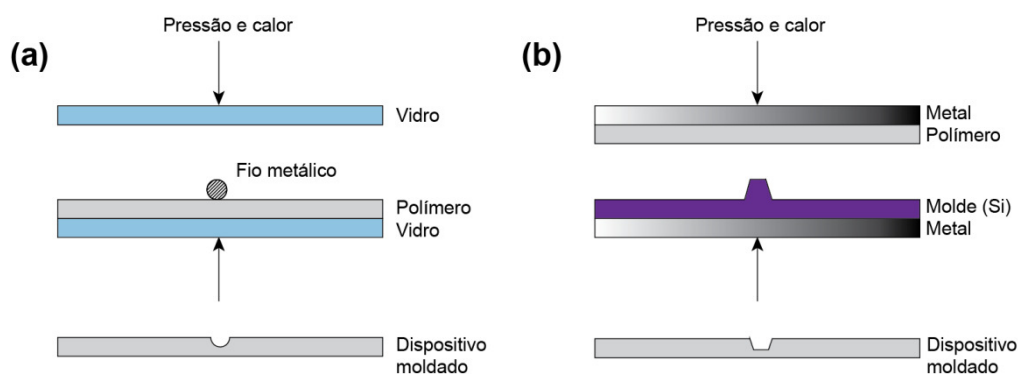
Moldagem por pressão a quente: a) Molde de fio metálico. b) Molde em silício ou quartzo [17]
